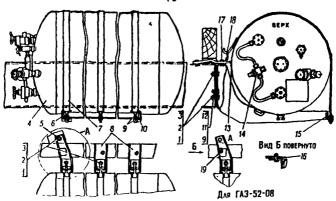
Установка баллона на автомобили ГАЗ-53-07 и ГАЗ-52-08
